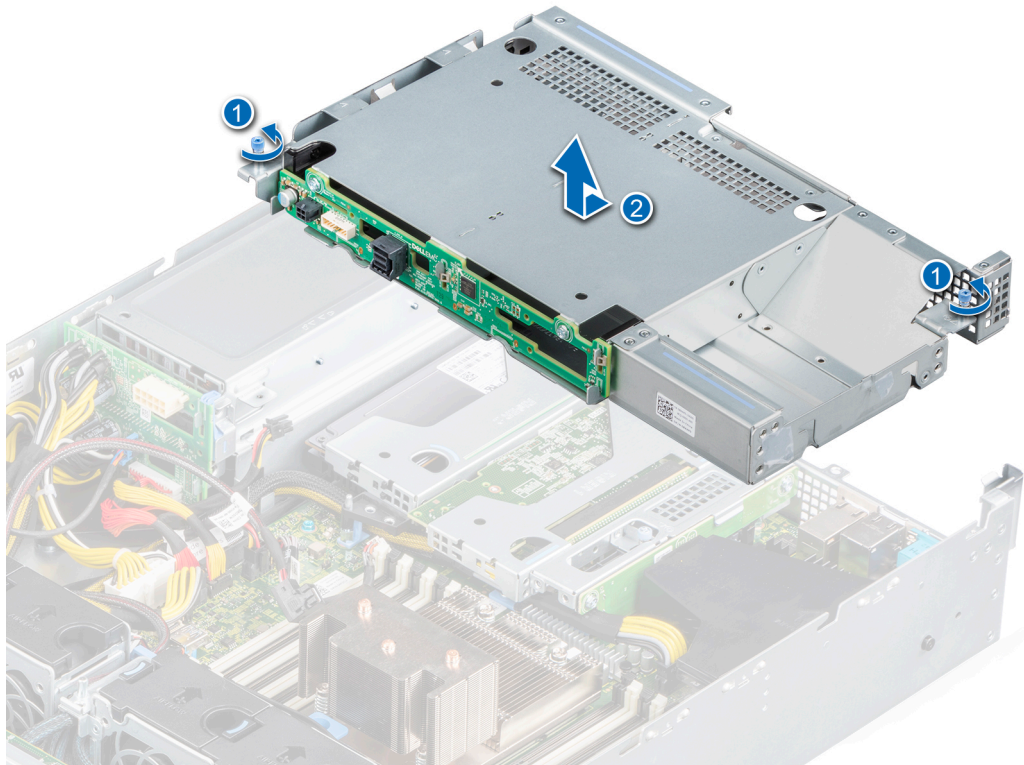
Entfernen des hinteren Laufwerksgehäuses
